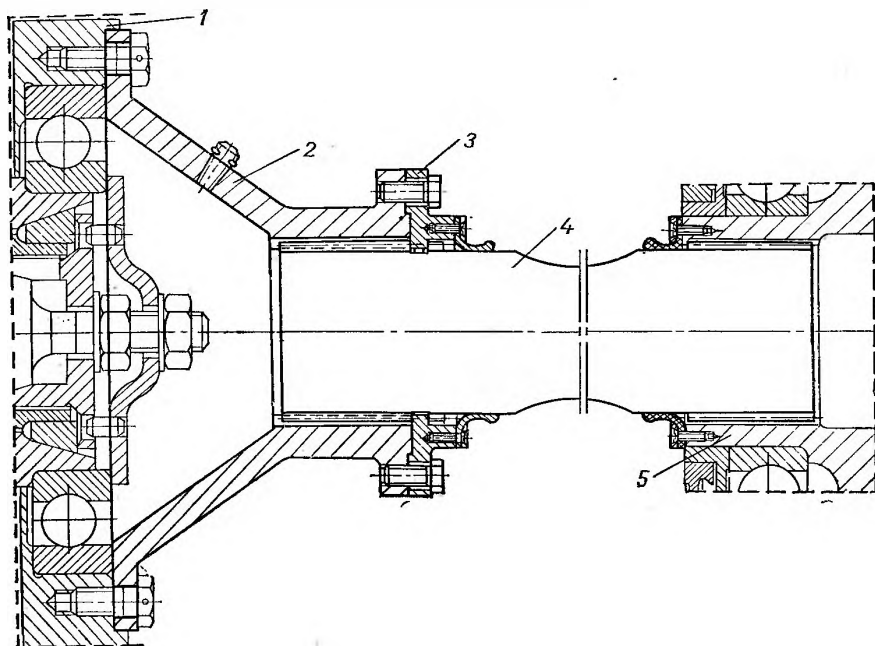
Первый карданный вал экскаватора ЭТР253
